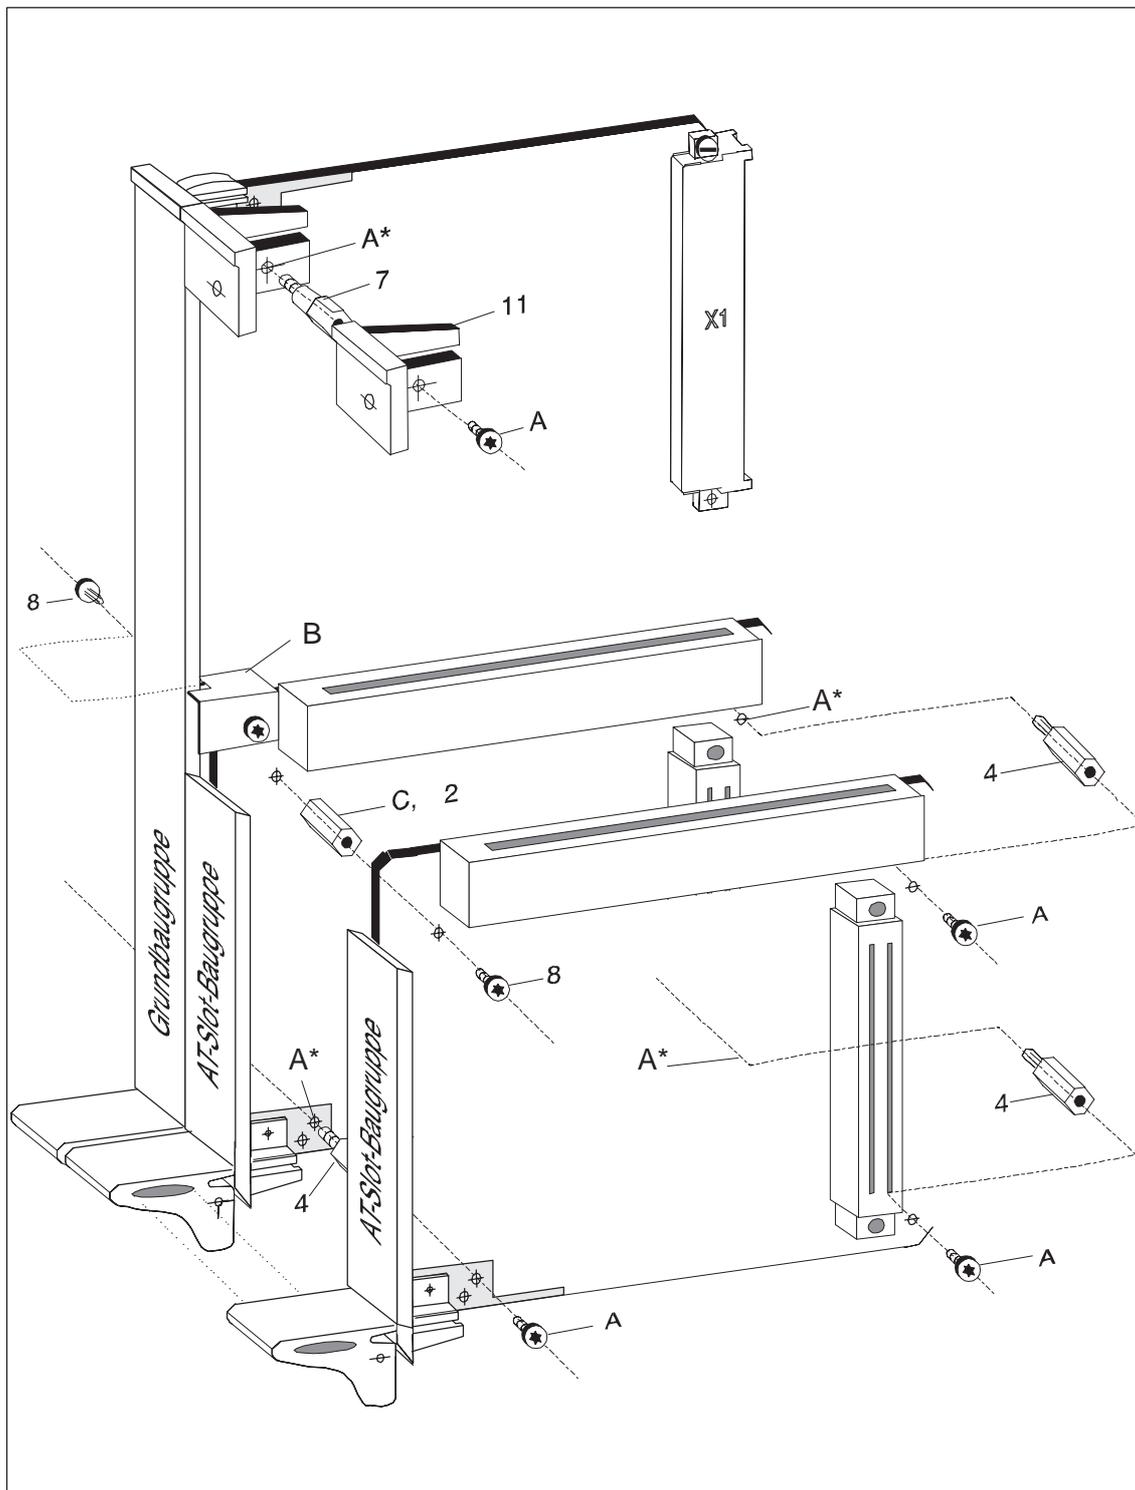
Montage von zwei AT-Slot-Baugruppen auf die Grundbaugruppe
